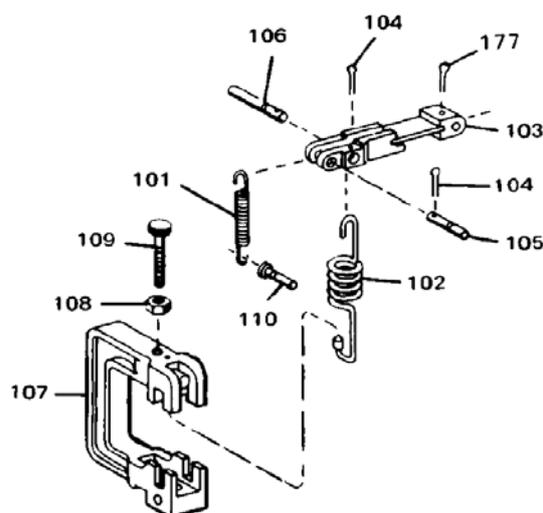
Покомпонентный чертеж регулировки низкой скорости
